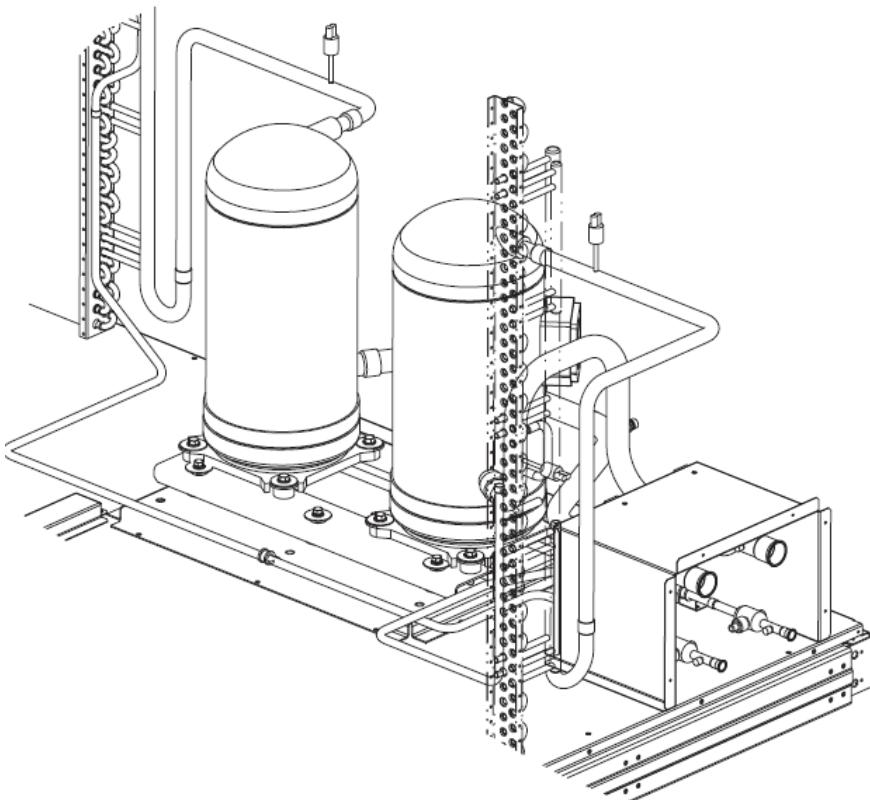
Модель 38AUD\*16 – компрессорный блок (вид сзади)
